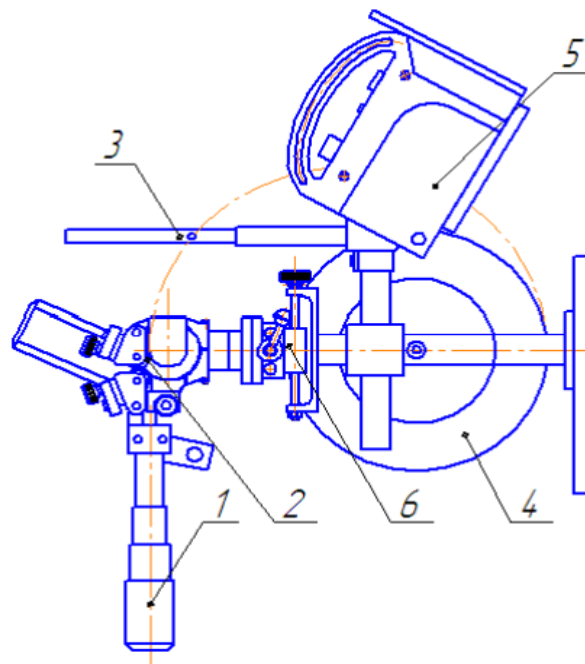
Зварювальна головка Мультитрак А2 (GMAW): 1 – пальник МТW600; 2 – механізм подачі; 3 – проміжний ролик подачі дроту; 4 – касета з дротом; 5 – блок керування; 6 – маховик регулювання положення зварювальної головки щодо шва.
